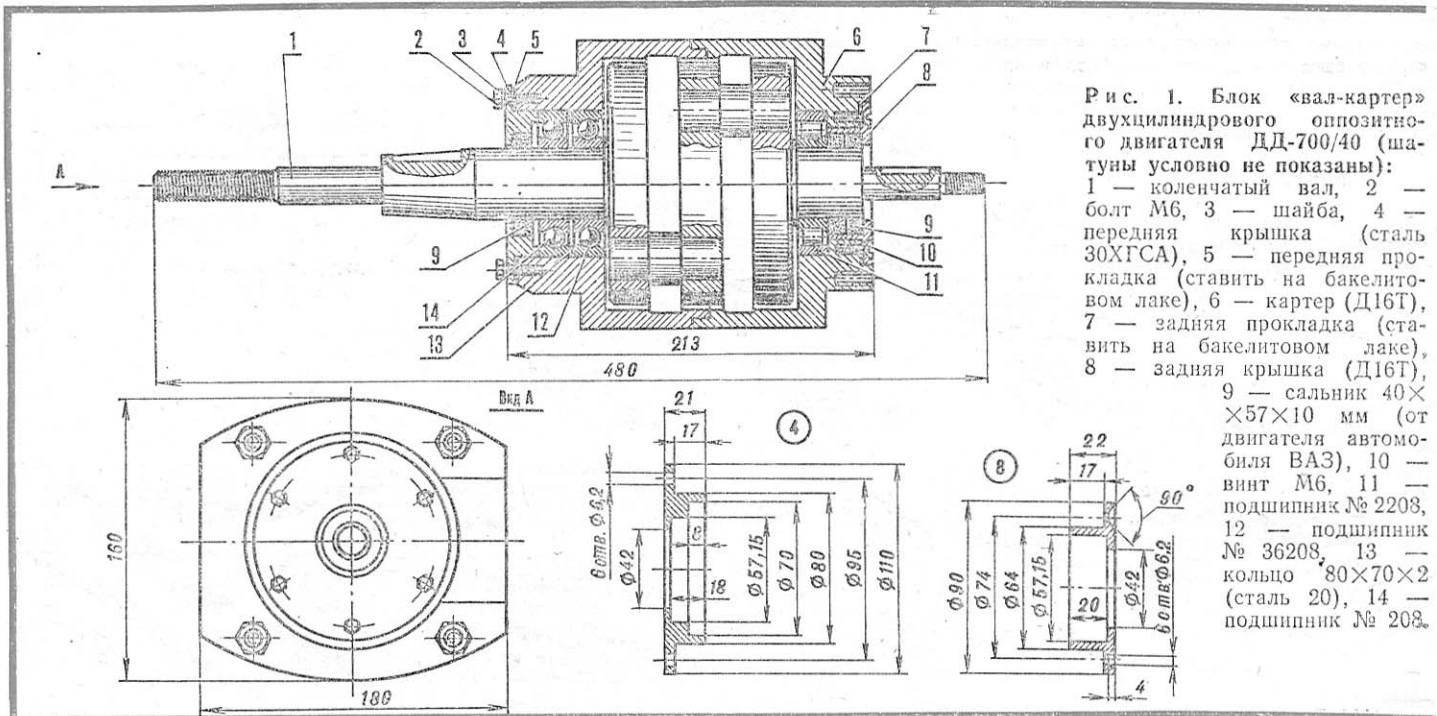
Блок «вал-картер» двухцилиндрового оппозитного двигателя ДД-700/40 (шатун условно не показаны): 1 — коленчатый вал, 2 — болт М6, 3 — шайба, 4 — передняя крышка (сталь 30ХГСА), 5 — передняя прокладка (ставить на бакелитовом лаке), 6 — картер (Д16Т), 7 — задняя прокладка (ставить на бакелитовом лаке), 8 — задняя крышка (Д16Т), 9 — сальник 40×57×10 мм (от двигателя автомобиля ВАЗ), 10 — винт М6, 11 — подшипник № 2208, 12 — подшипник № 36208, 13 — кольцо 80×70×2 (сталь 20), 14 — подшипник № 208.
